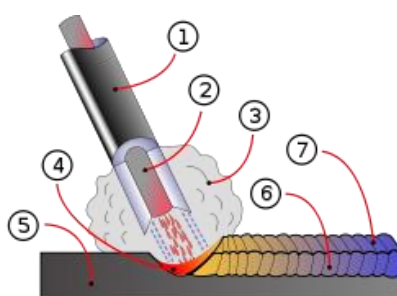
Сварка в защитных газах: 1 – горелка, 2 – электрод, 3 – защитный газ, 4 – место расплава металла, 5 – заготовка, 6, 7 – сварной шов [3]
